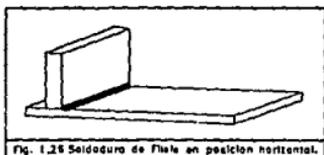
Soldadura de Filete en posición horizontal.
